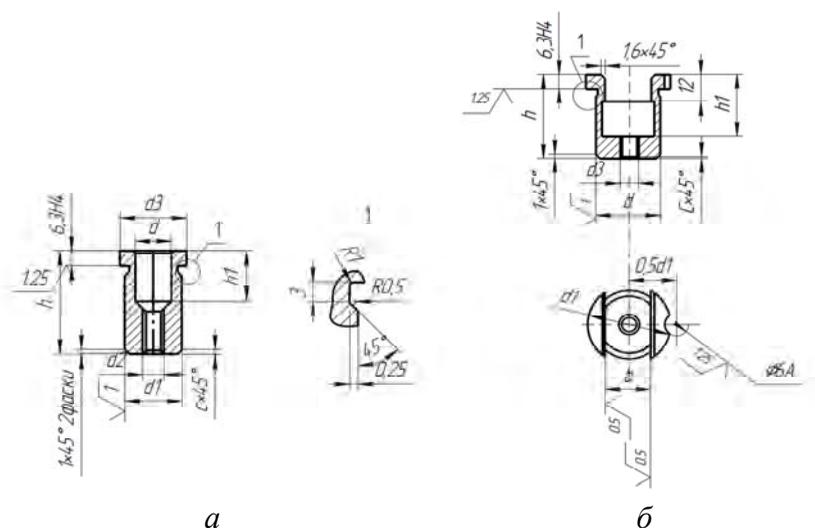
Конструкция центрирующей и направляющей втулок с резьбовым отверстием:
